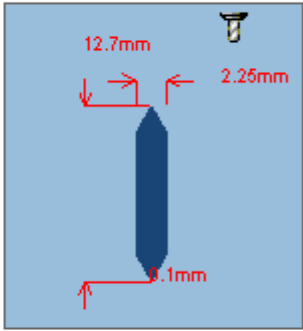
Пластинка резца «266RG-16MM01A300M 1125»
